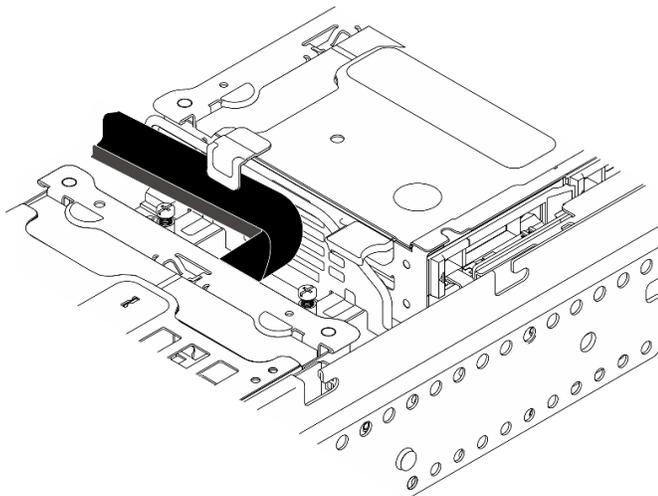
Disposición de los cables de la placa posterior de la unidad frontal
